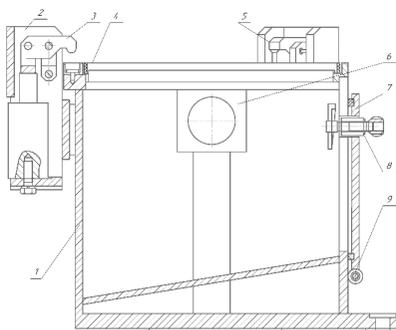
Общая конструкция стенда для испытания главной передачи:
